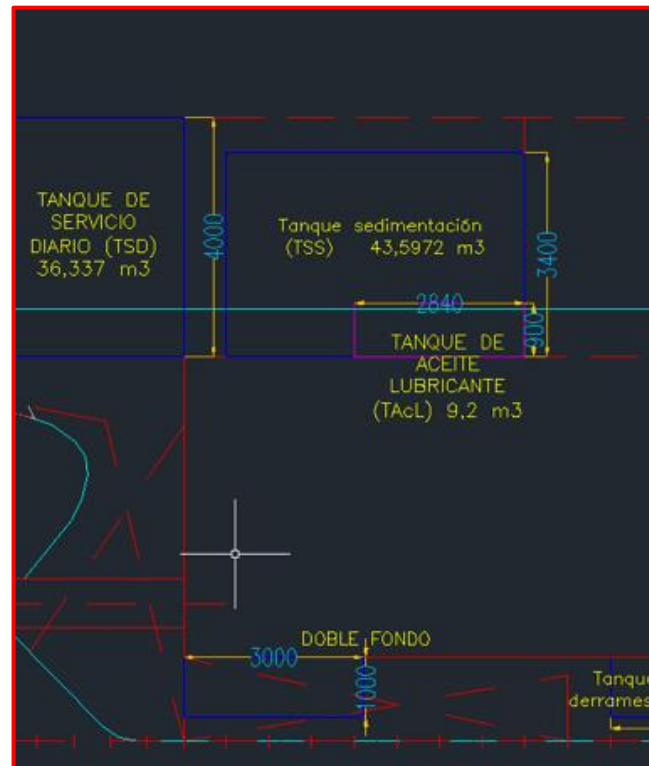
Tanque sedimentación / vista estribor (alzado)
